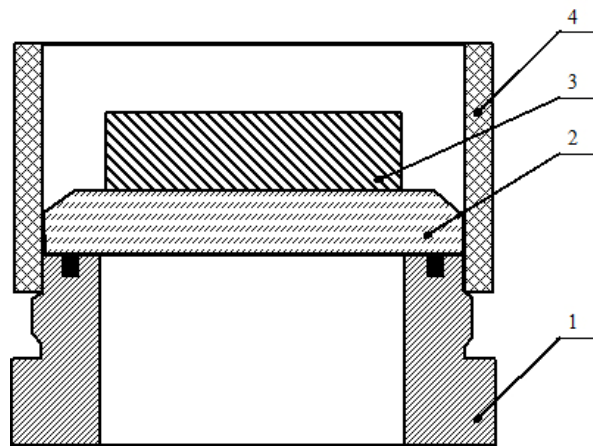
Схема збірки для паяння кварцового скла з алюмінієвим фланцем: 1 — алюмінієвий фланець; 2 — кварцове скло; 3 — металевий вантаж; 4 — графітове кільце
